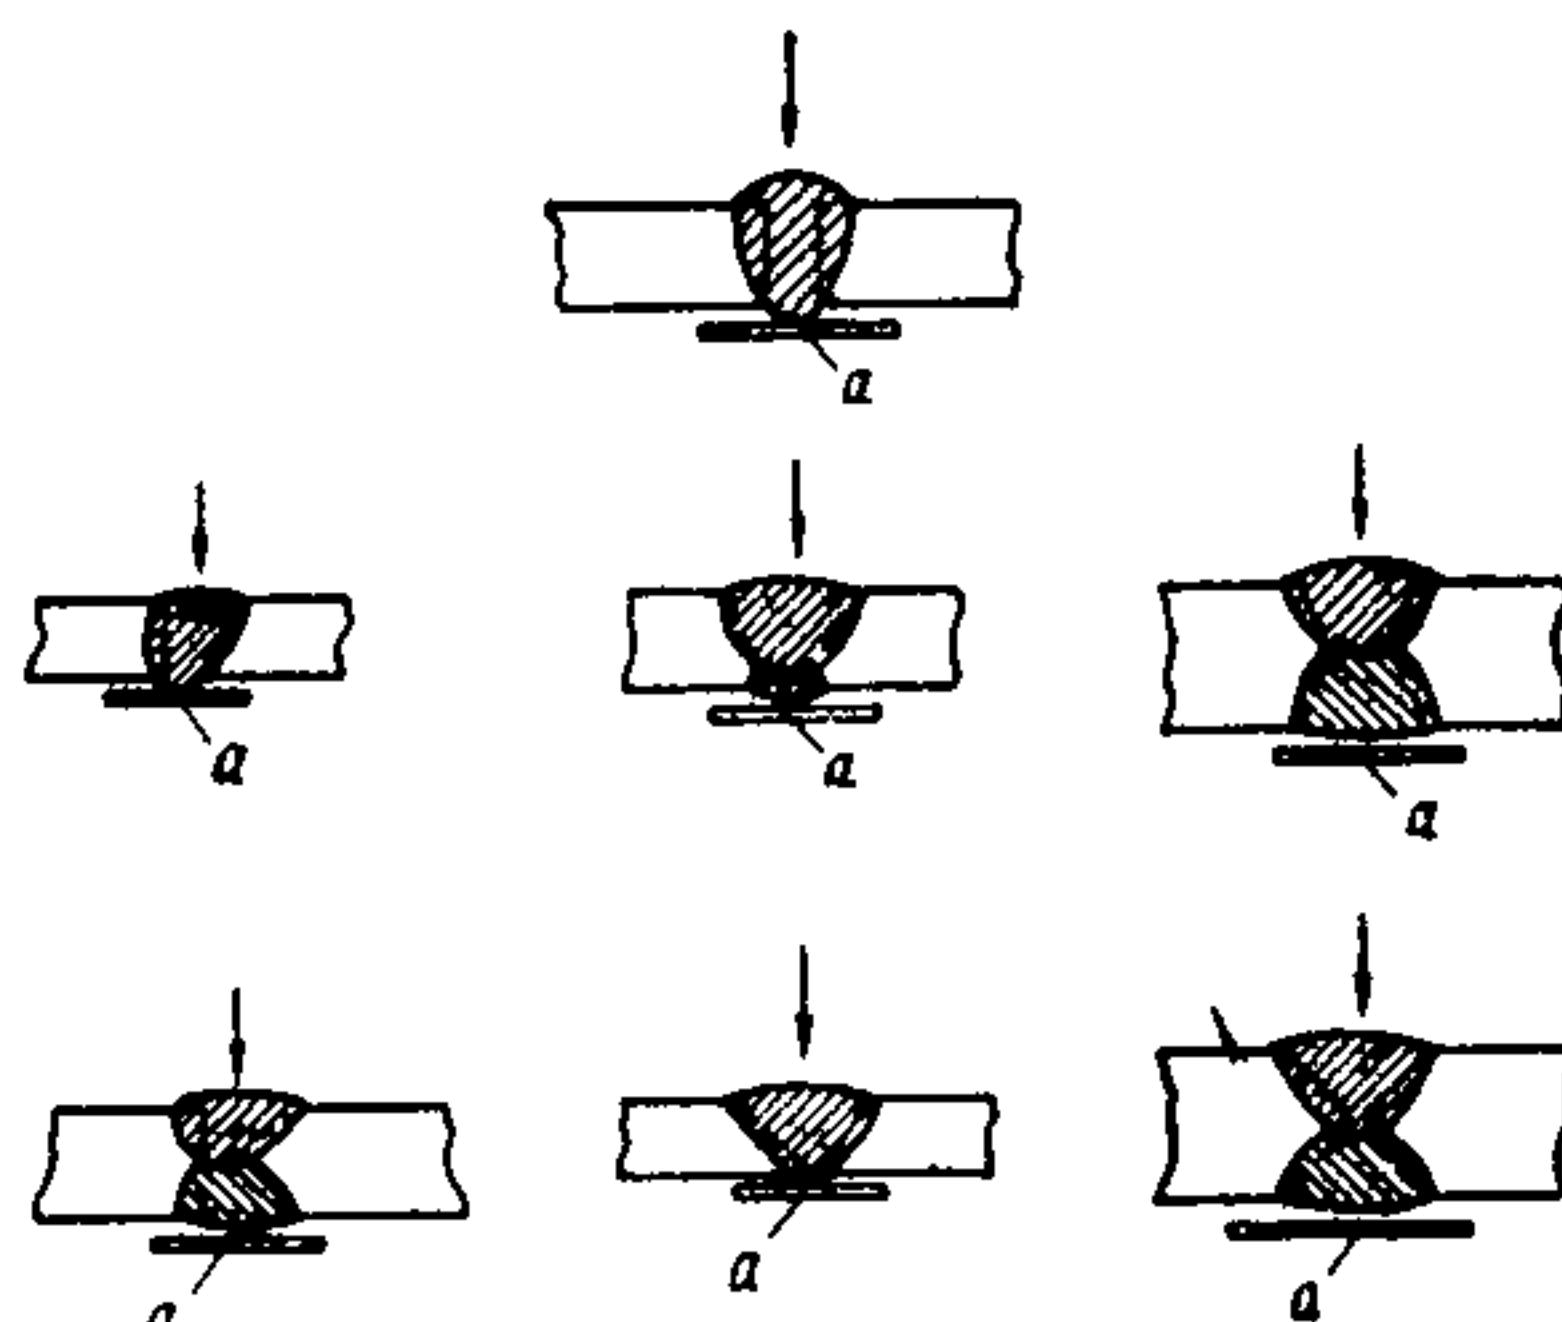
Схемы просвечивания стыковых сварных соединений с различной подготовкой
